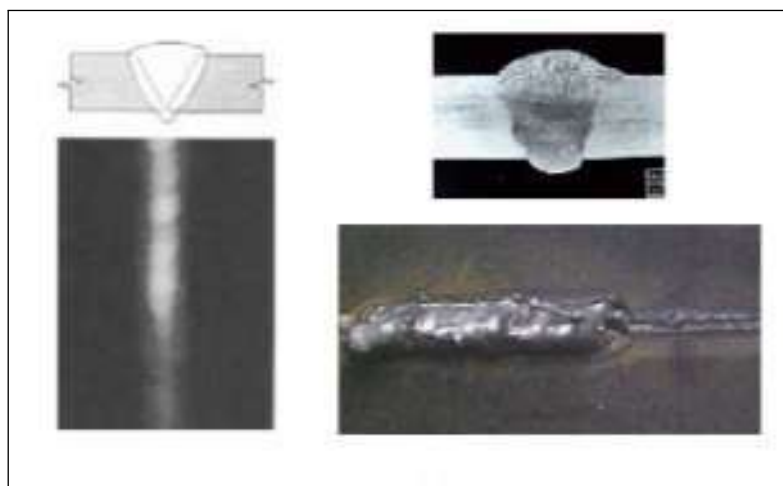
Exceso de penetración de la soldadura.
